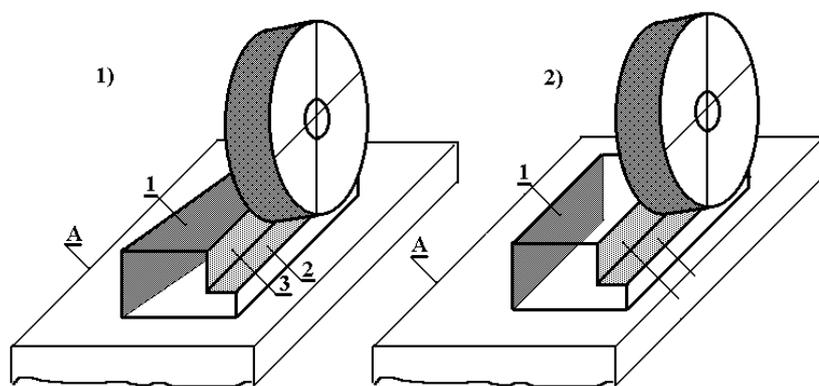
Установка заготовки на магнитный стол. Если заготовка устанавливается на магнитный стол достаточно произвольно (вариант 1), то условие параллельности поверхностей 1 и 3 может быть не выполнено и одновременно не будет достигнута равная ширина поверхности 2. Если же с помощью приборов поверхность 1 заготовки будет строго выверена по параллельности кромки А магнитного стола (вариант 2), то условие параллельности поверхностей заготовки 3 и 1 и равная ширина поверхности 2 будут выполнены. Таким образом, поверхность 1 служит базой, относительно которой производится установка заготовки на магнитном столе станка.
